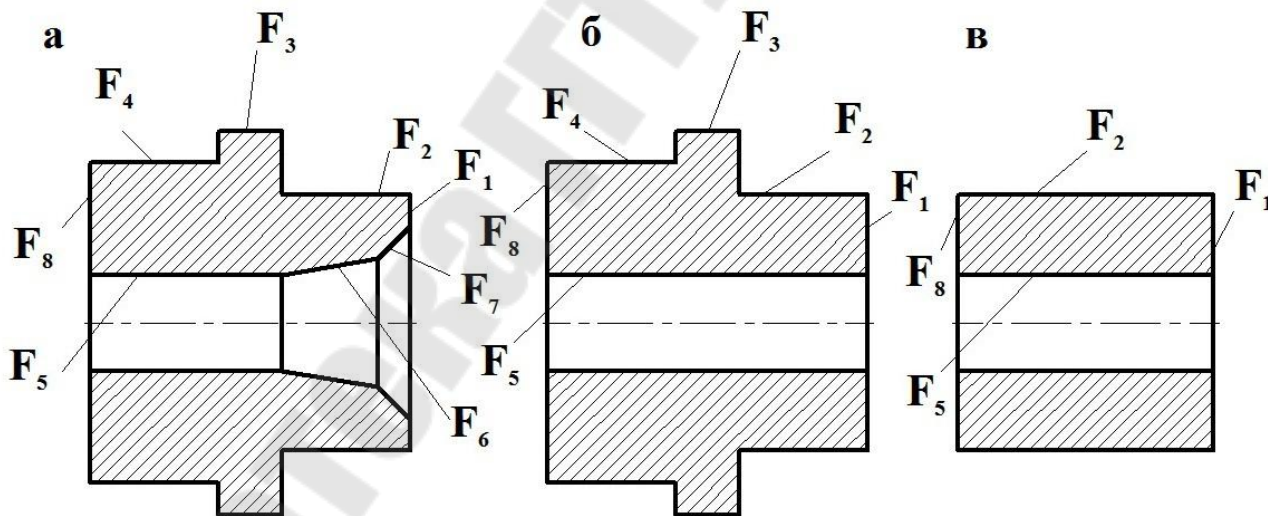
Эскизы заготовок деталей при токарной обработке
